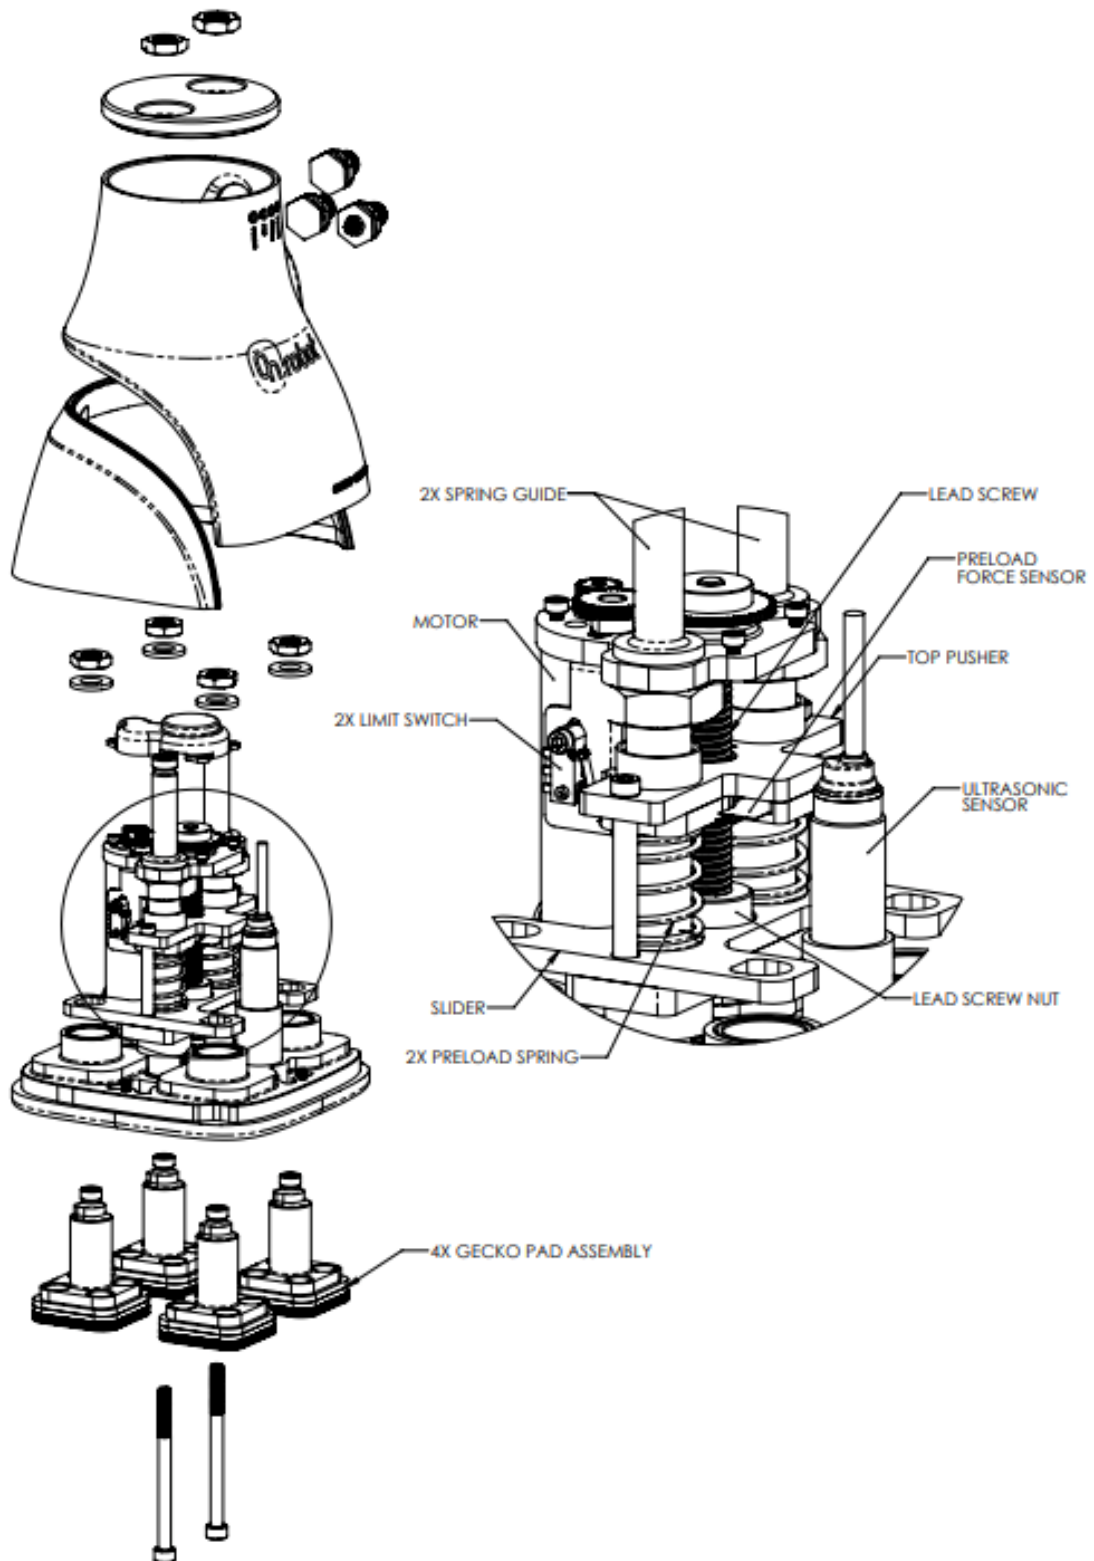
Disegno CAD della pinza Gecko e dei cuscinetti.
